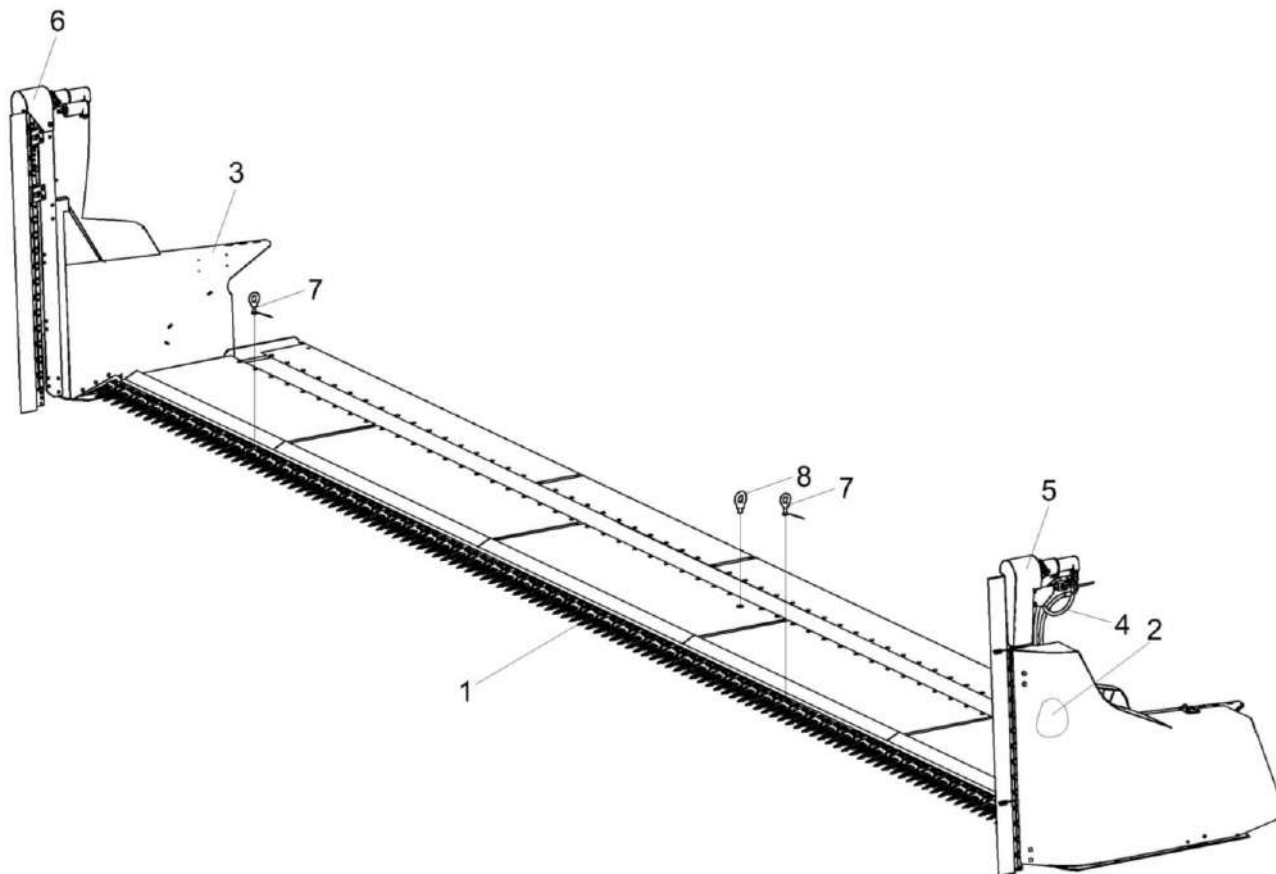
Приспособление для уборки рапса КЗК-9-1-1540000 (лист 1)
